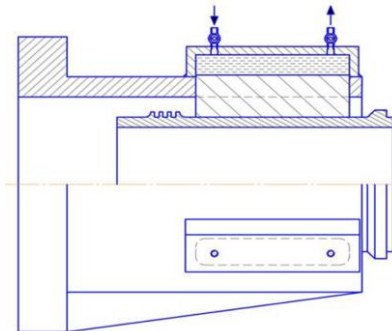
Схема конструкції пристосування для установки циліндрової втулки при вібророзкатуванні
